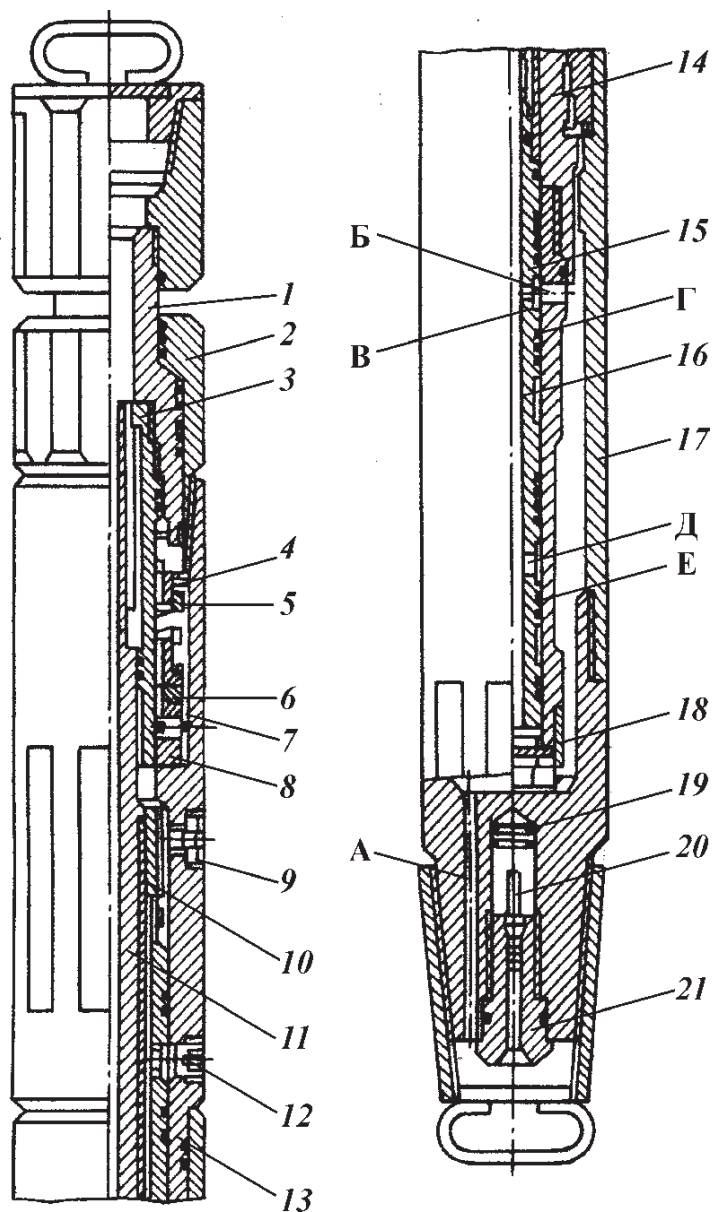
Запорно-поворотный клапан КЗ-145:
